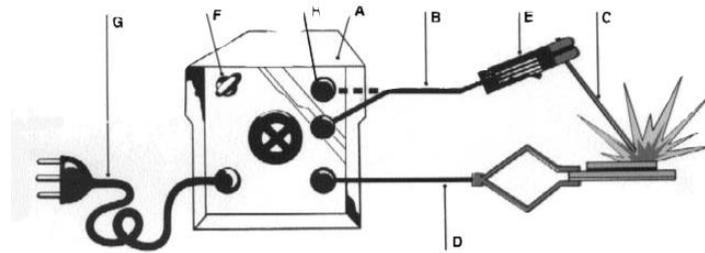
SOLDADURA ELÉCTRICA
